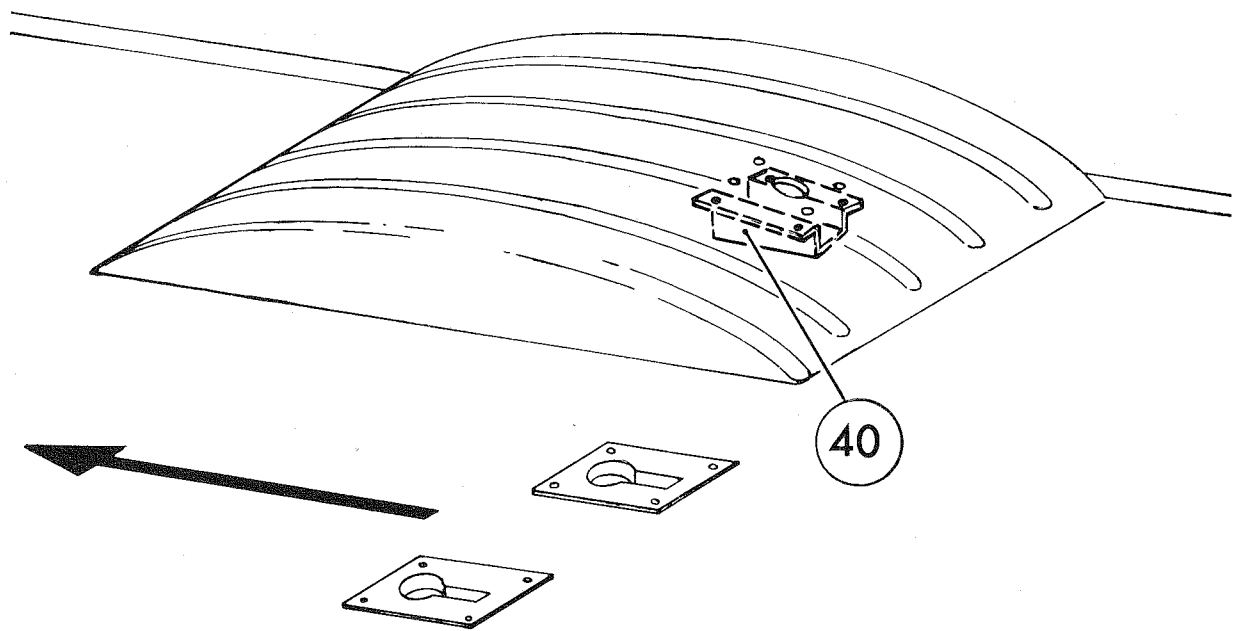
Einbaumaße für Sockel rechter Schrank und Sockel Stromerzeugerkasten.
